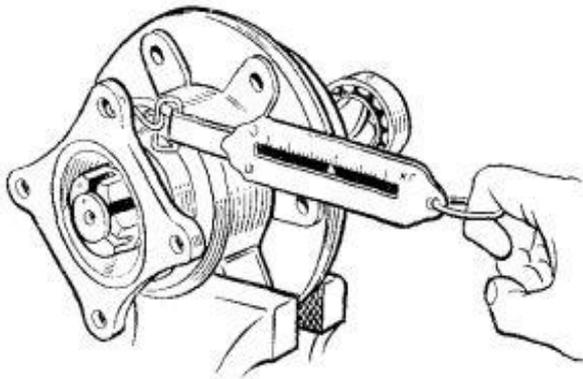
Проверка затяжки подшипников ведущей шестерни
